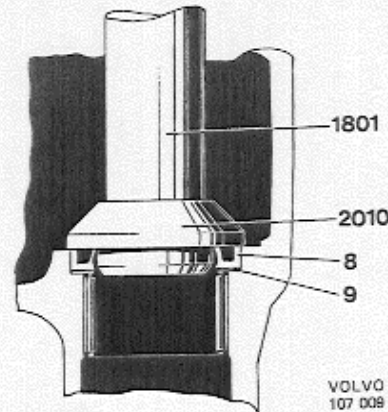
Einpressen des oberen Wellendichtringes, Segmentwelle
